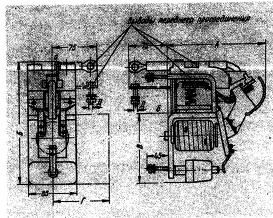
Габаритные и установочные размеры контакторов с Н3 контактами, с гашением, на номинальный ток 150 а, типа КП 523 и 300 а, типа КП 524, с задним и передним присоединением
